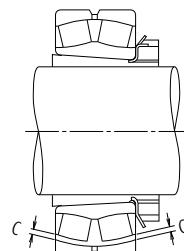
Medición del Juego de los Rodamientos de Rodillos Esféricos
